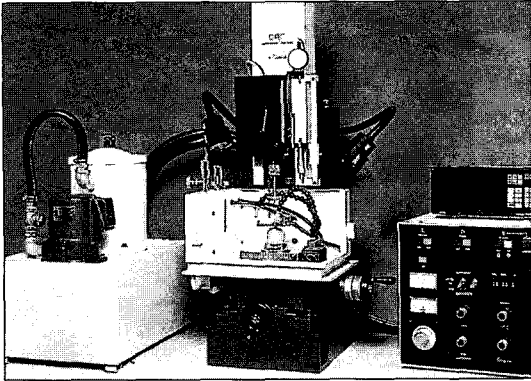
치과기공용 EDM 장비인 SAE-2000. Machining unit, oil과 filter system, 그리고 generator와 control box로 구성되어 있다.
